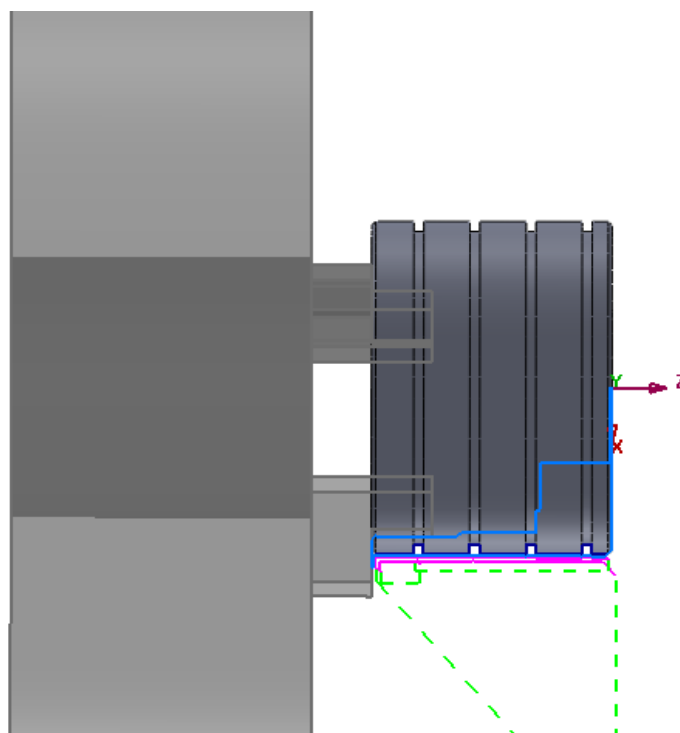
чорнове точіння зовнішньої циліндричної поверхні
